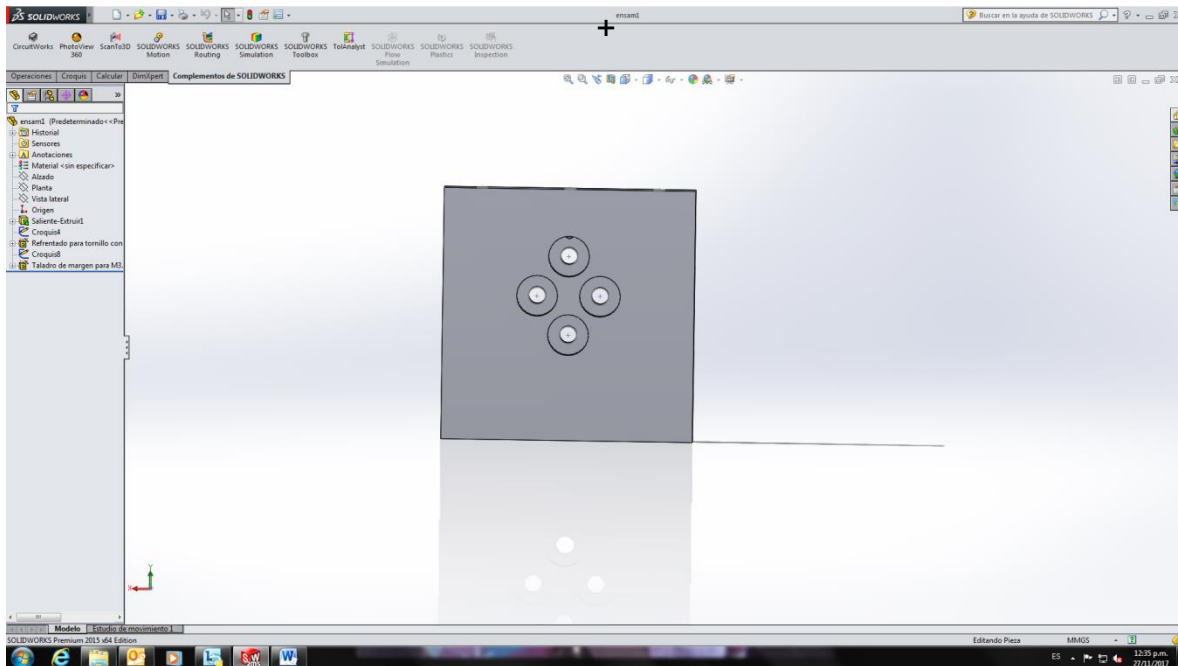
diseño de base para cámaras CV-500CA en solidworks
